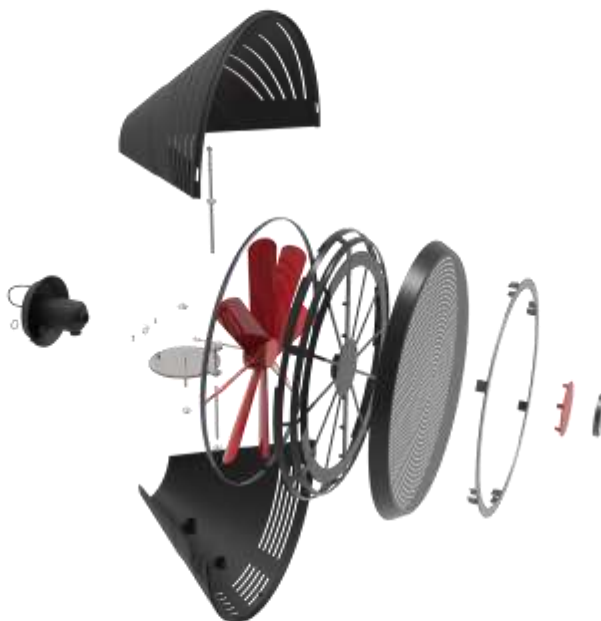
Vista explodida do ventilador. Fonte: Autor.
